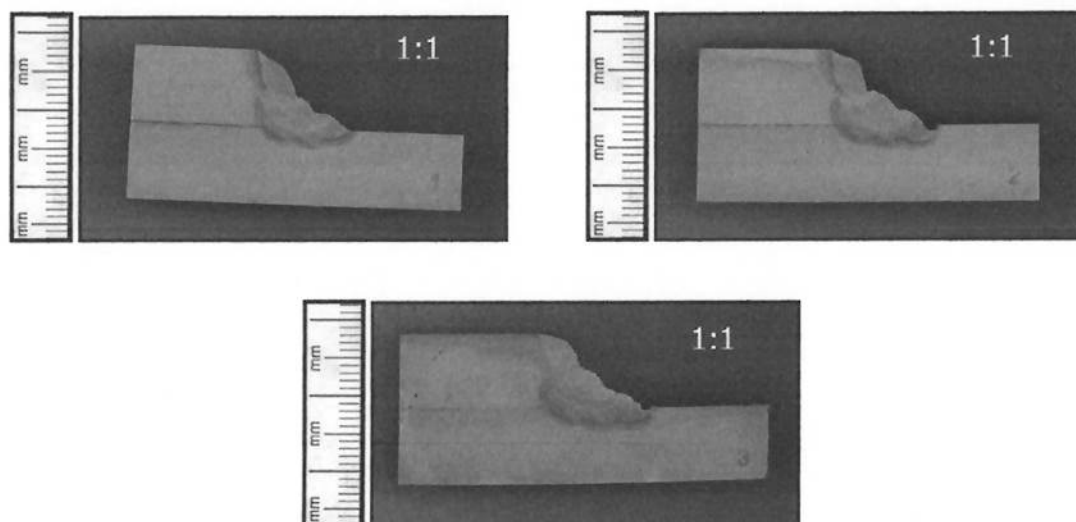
Ensaio de macrografia da junta soldada com energia de soldagem intermediária (0,63 kJ/mm).
